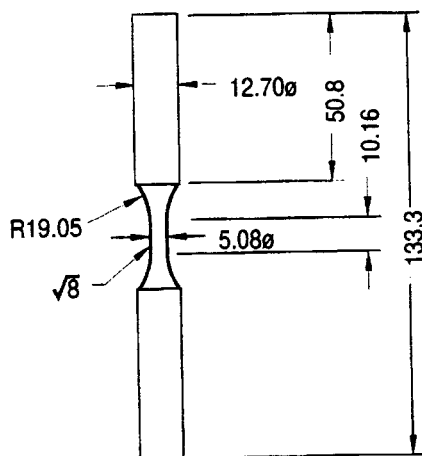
Eprouvette de fatigue-torsion [BON99].
